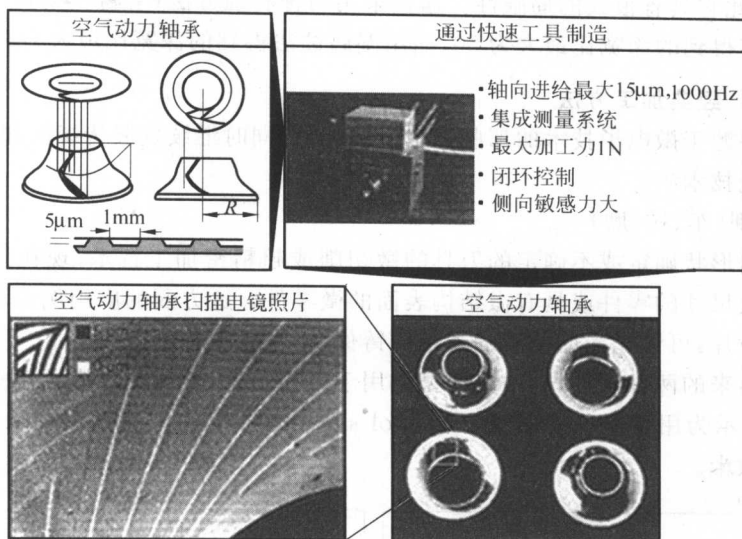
用快速工具系统加工的空气动力轴承的微结构
